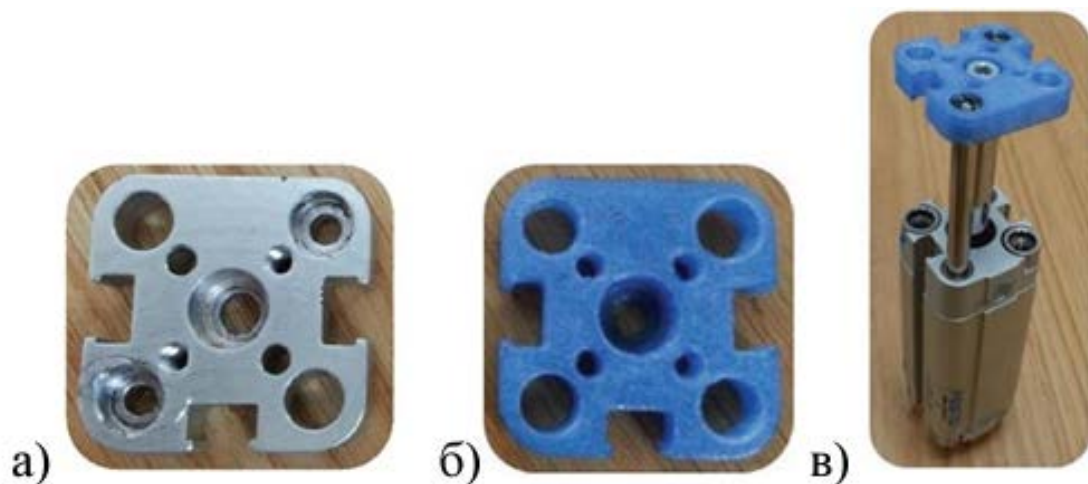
Заміна коромисла пневматичного циліндра верстата для виробництва відкидних дисків: а - оригінальна деталь коромисла, алюміній; б - деталь коромисла, виготовлена на 3D-принтері з PLA пластику; в - пневматичний циліндр у зборі
